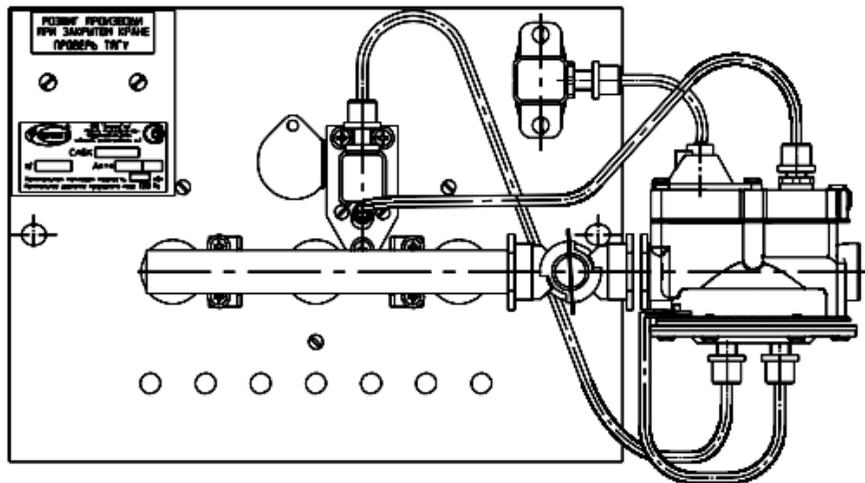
Общий вид автоматики САБК-9.5-РД
